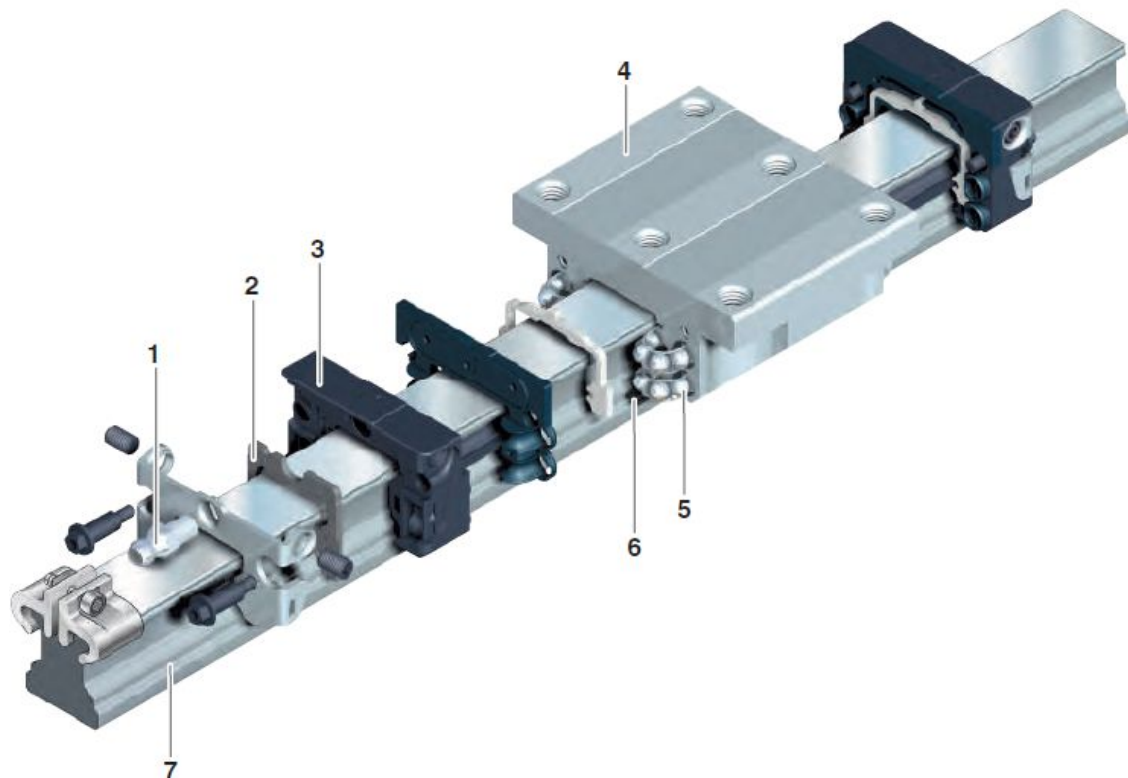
Конструкція кульковою рейкової направляючої останнього покоління
